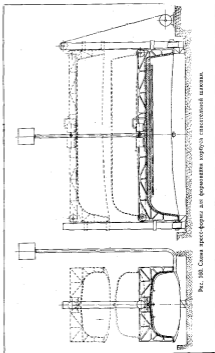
Схема пресс-формы для формирования корпуса спасательной шлюпки.
